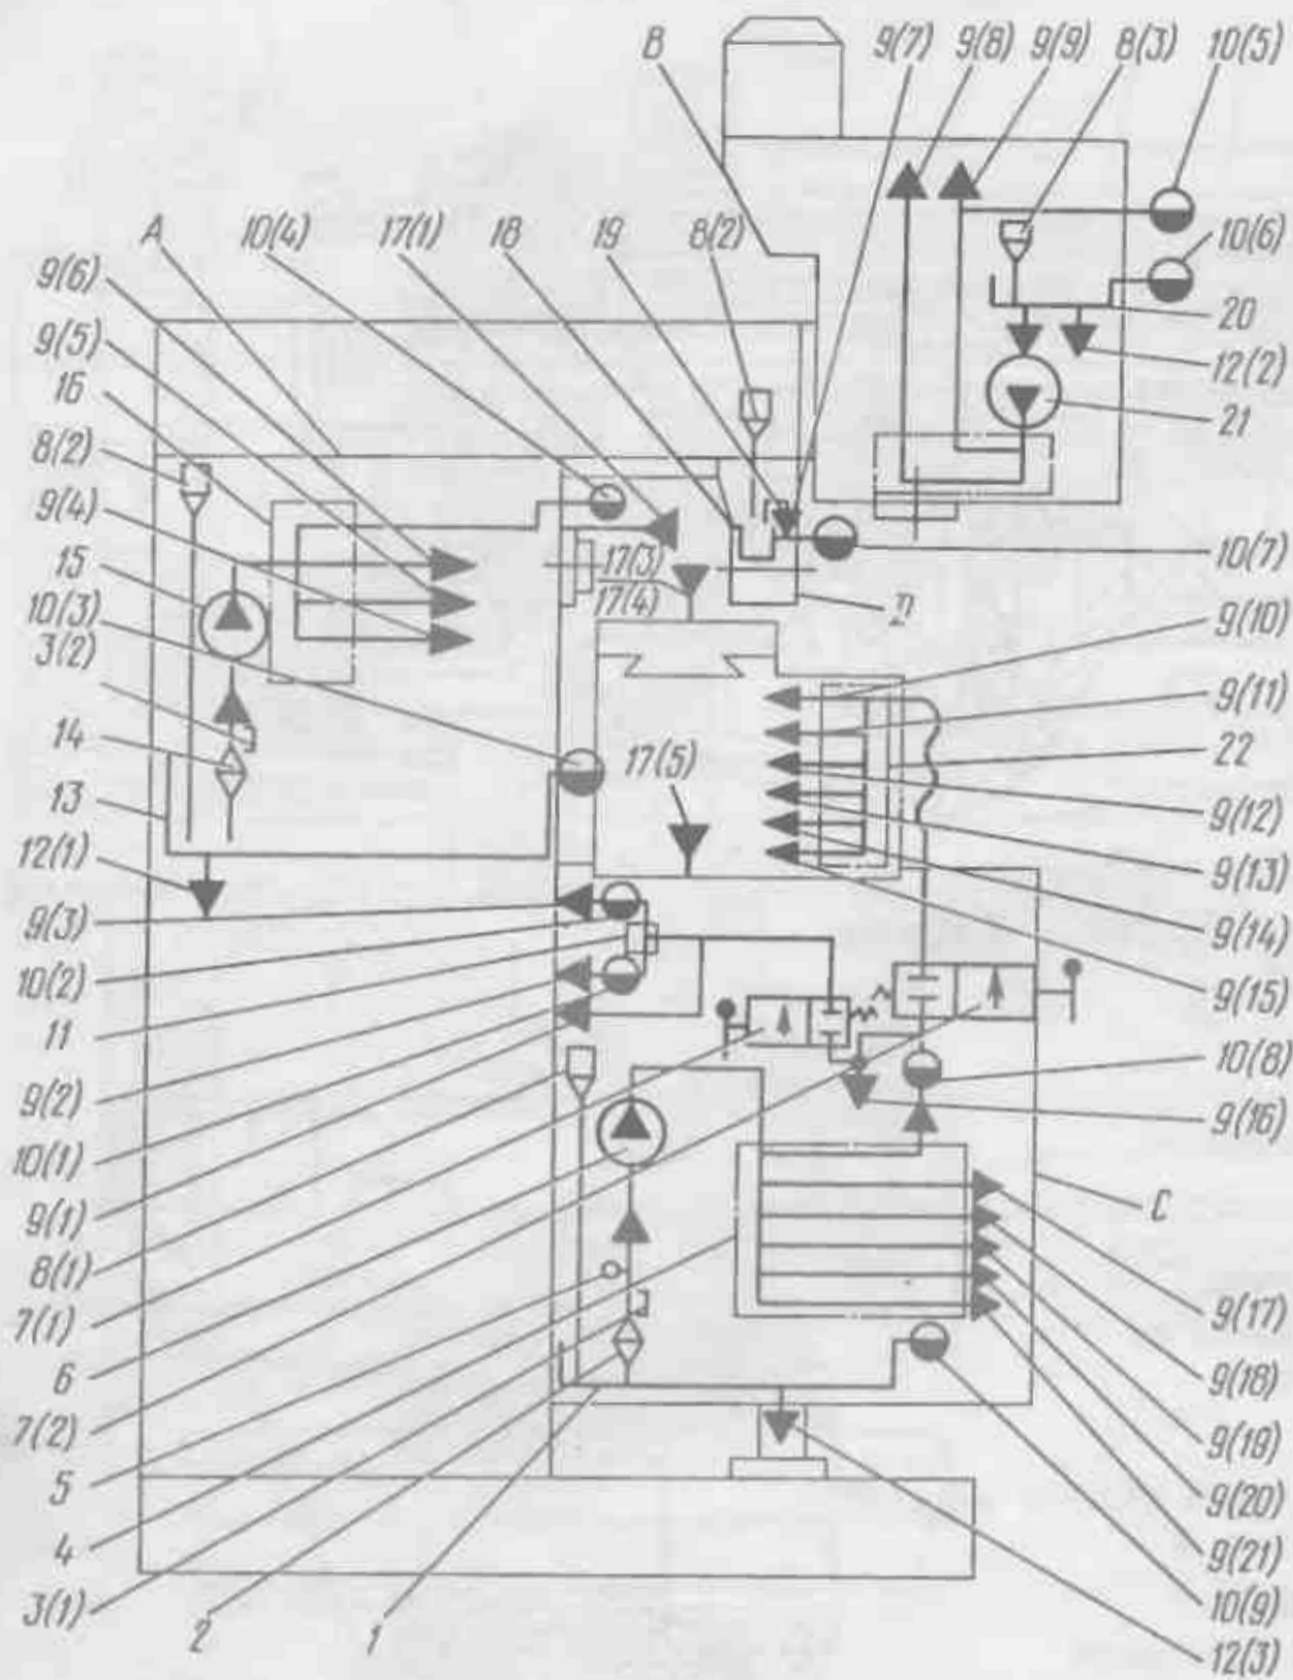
Принципиальная схема смазки станка 6Т80М:
